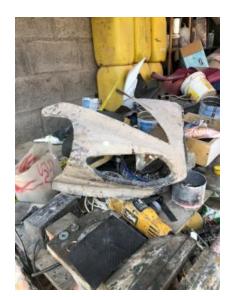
Molde de motopieza y Pieza acabada y montada. Diseños exclusivos de Ramiro Trujillo dueño de TRUMAN moto tunning
